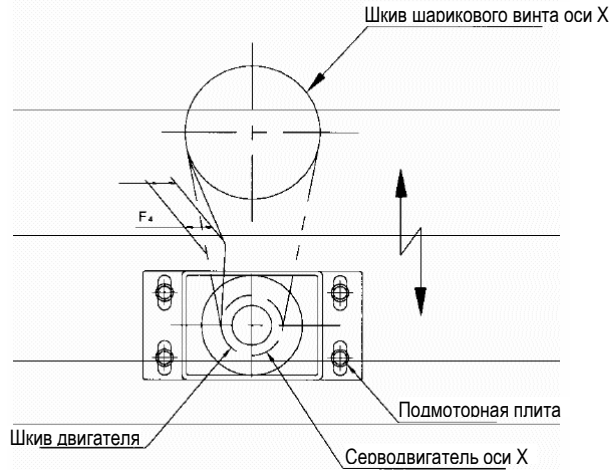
Зубчатый ремень привода для серводвигателя оси X
